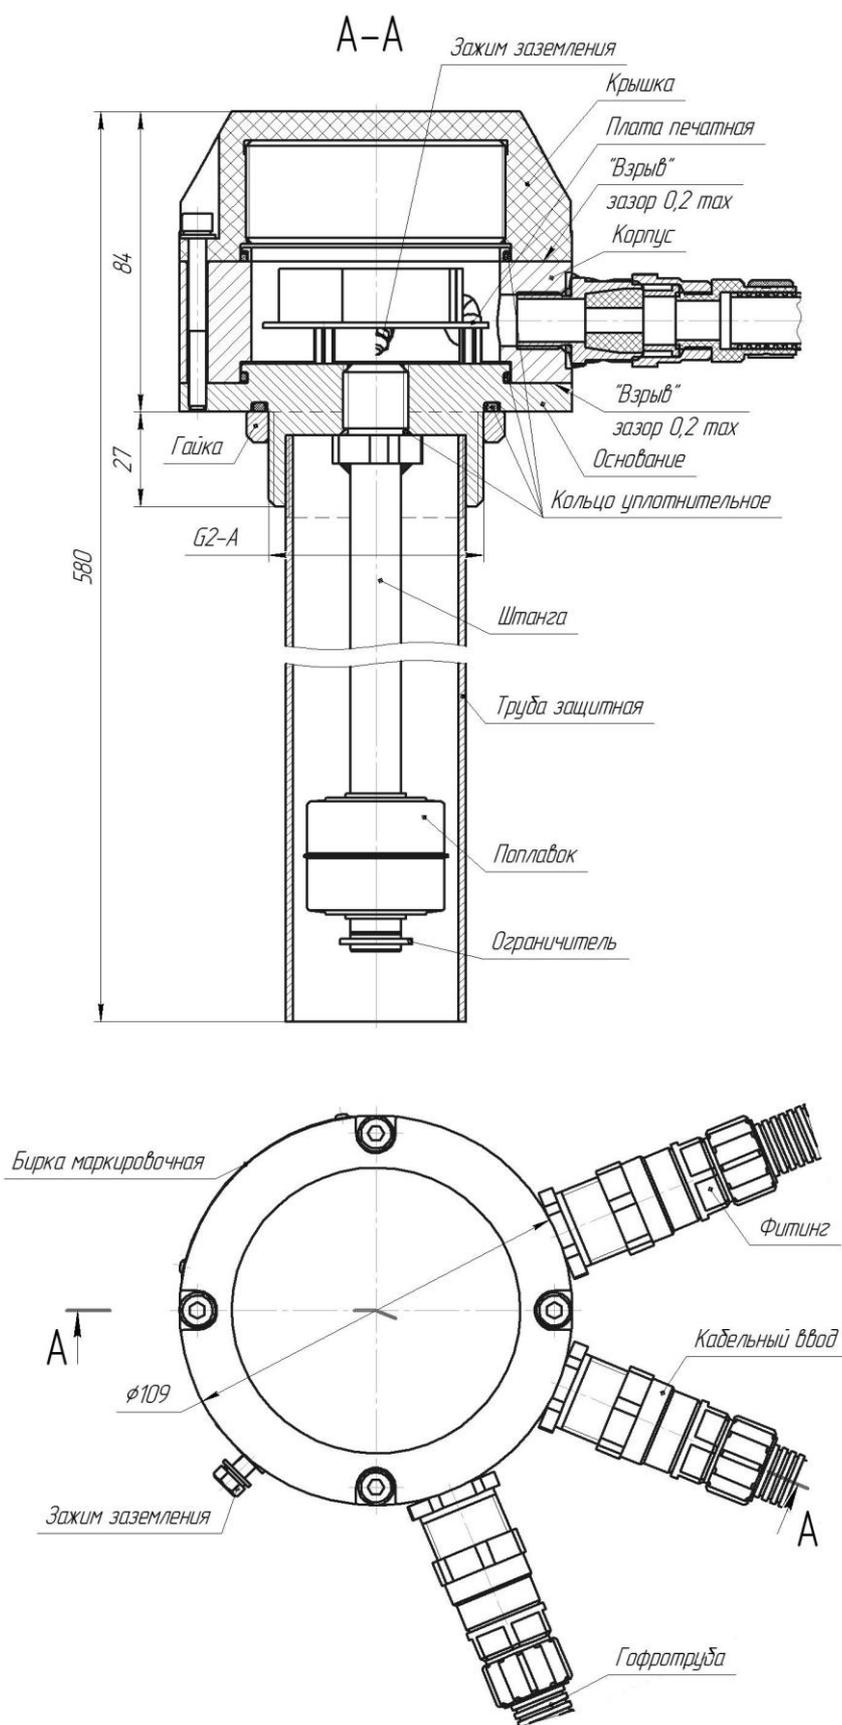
Габаритные и присоединительные размеры ДЛОК-У-1-GPS II
